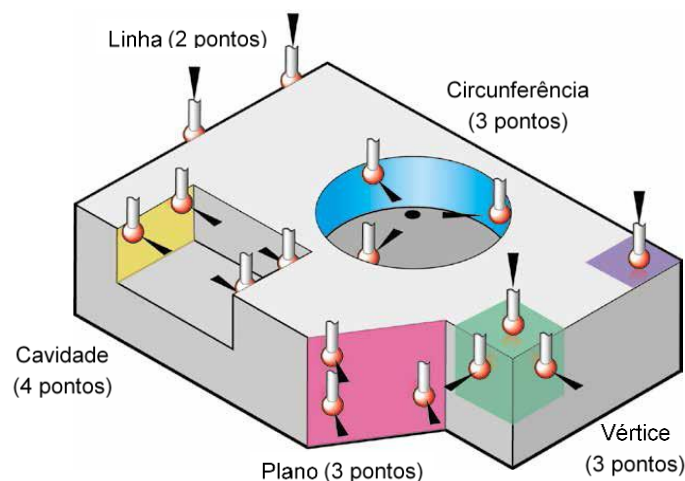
Número de pontos que descrevem as formas geométricas (Renishaw, Probing systems for CNC machine tools, 2014)
